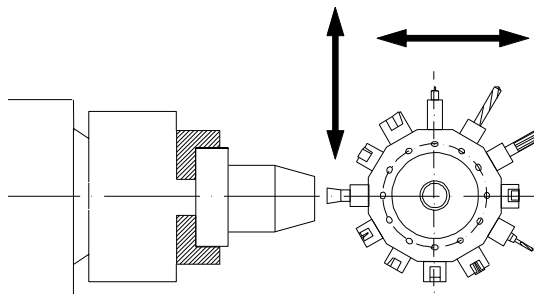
А. Напрями рухів подач токарного верстата з ЧПК
